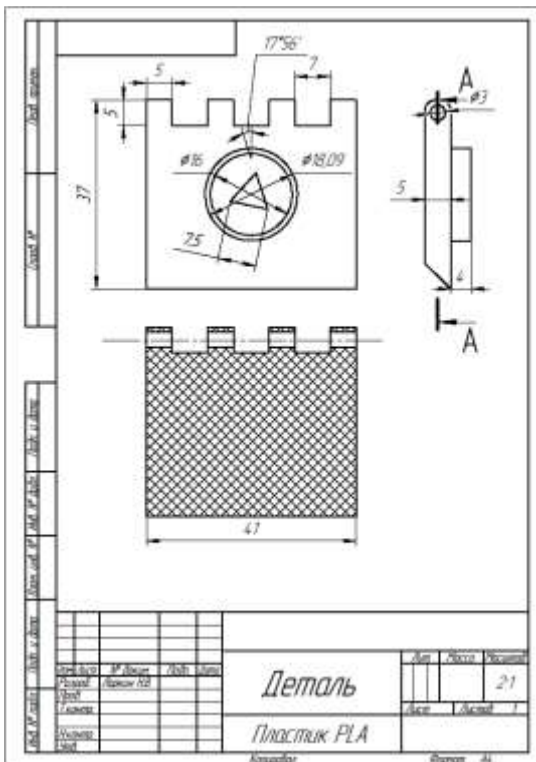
Чертеж деталей коробочки из практического задания для 10-11 классов, выполненный в программе Компас3D
